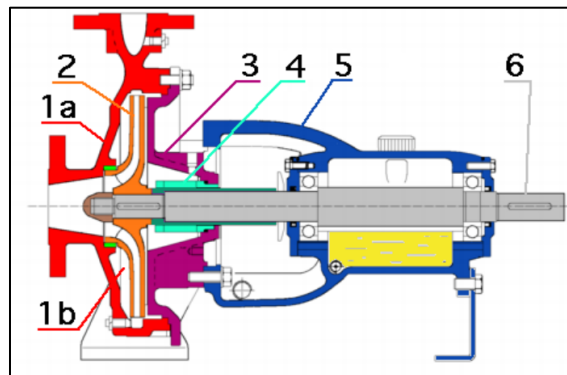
Corte esquemático de una bomba centrífuga: 1a carcasa o cuerpo de la bomba, 1b cámara de la bomba, 2 rodete o impulsor, 3 cajera del cierre del eje, 4 camisa del cierre del eje, 5 soporte y carcasa de rodamientos, 6 eje. Tomado de Wikipedia (Wikipedia, 2010).
